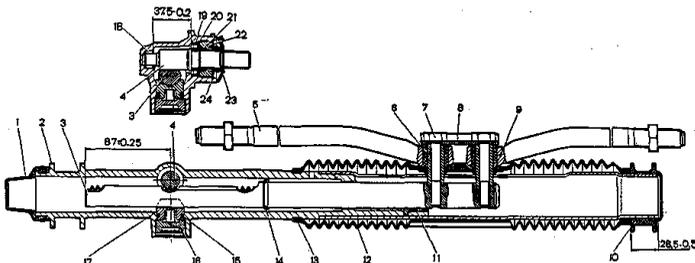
Разрез рулевого механизма: 1 - защитный колпак; 2 • картер рулевого механизма; 3 - рейка; 4 - приводная шестерня; 5 - внутренний наконечник рулевой тяги; 6 - распорная втулка; 7 • болт крепления рулевой тяги; 8 - соединительная пластина; 9 • опорная втулка; 10 - опора рулевого механизма; 11 - опорная втулка рейки; 12 - защитный чехол; 13 - хомут; 14 - ограничительное кольцо рейки; 15 • уплотнительное кольцо упора рейки; 16 • гайка; 17 - упор рейки; 18 - роликовый подшипник; 19 - шариковый подшипник; 20 - стопорное кольцо; 21 - уплотнительное кольцо гайки; 22 • гайка крепления подшипника шестерни; 23 • пыльник; 24 • стопорная шайба
